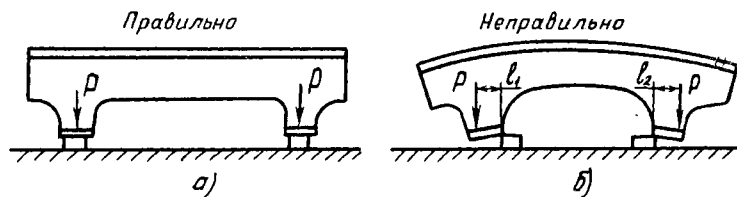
Влияние местоположения точек приложения сил закрепления на погрешность установки заготовки
